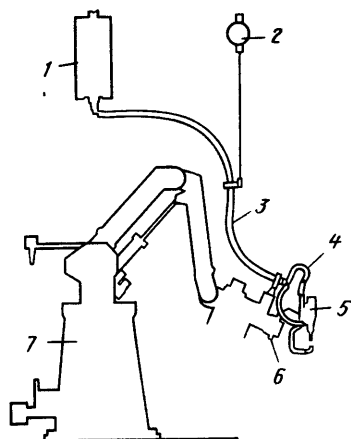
Вспомогательное оборудование сварочной ячейки:
